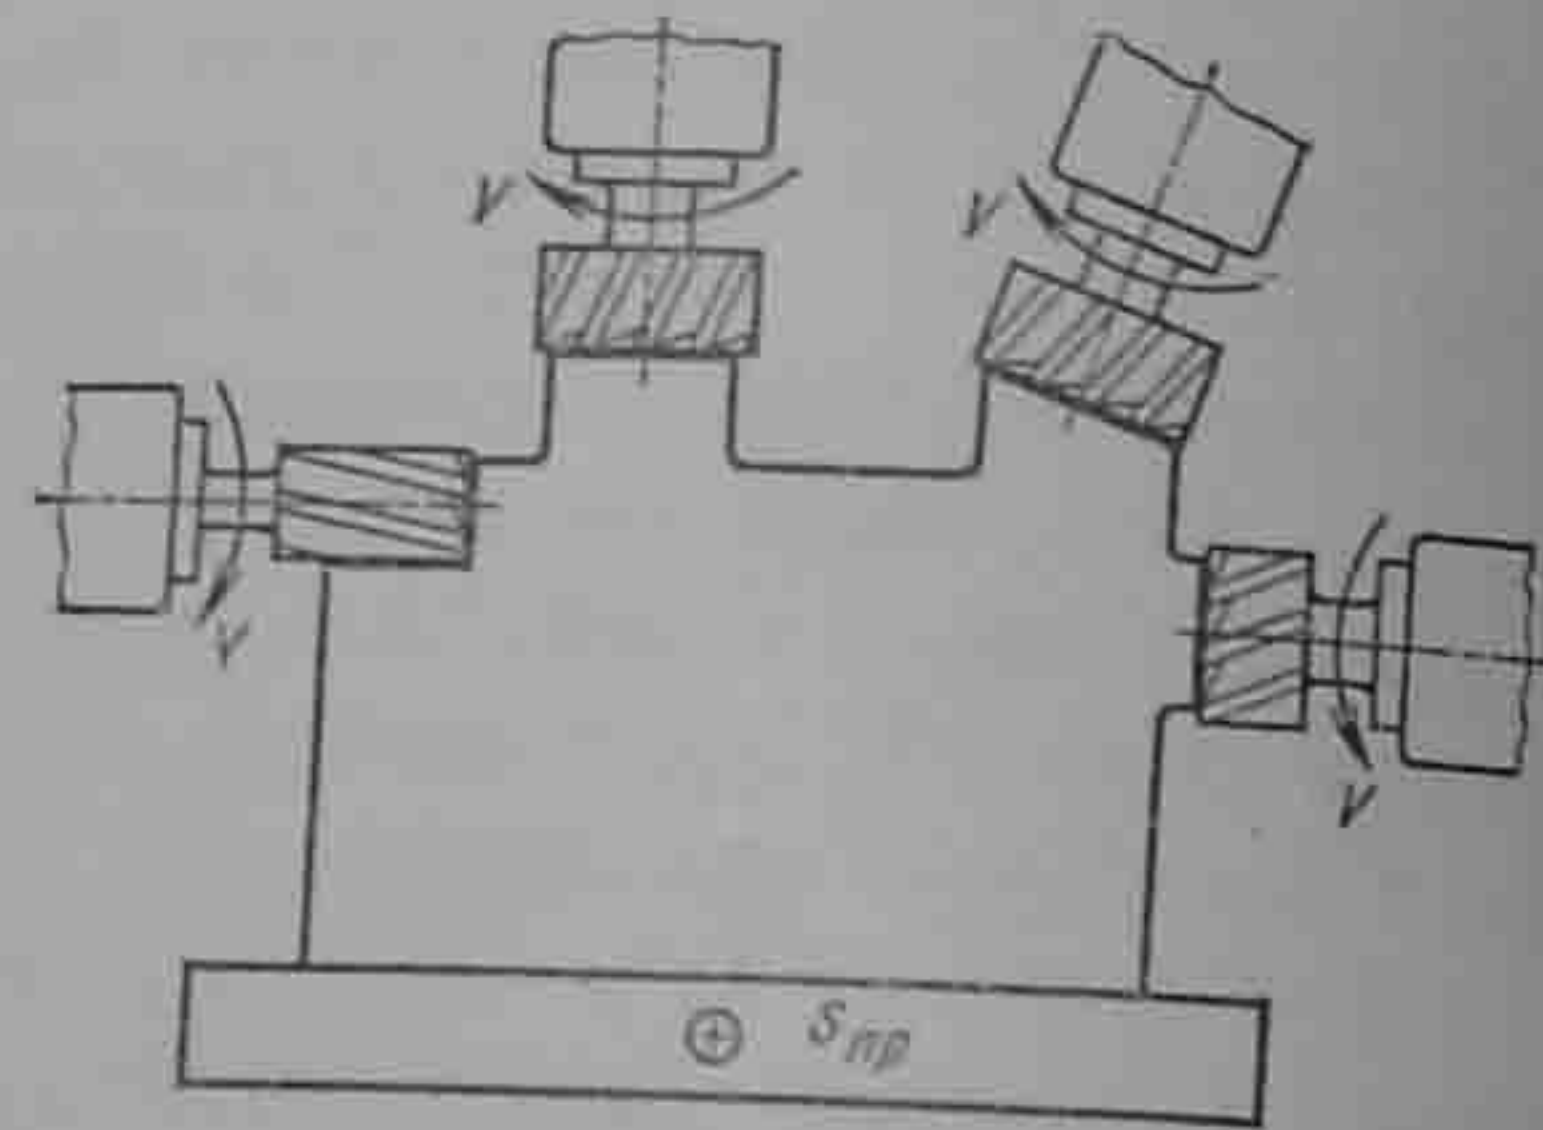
Схема обработки заготовки на продольно-фрезерном станке
